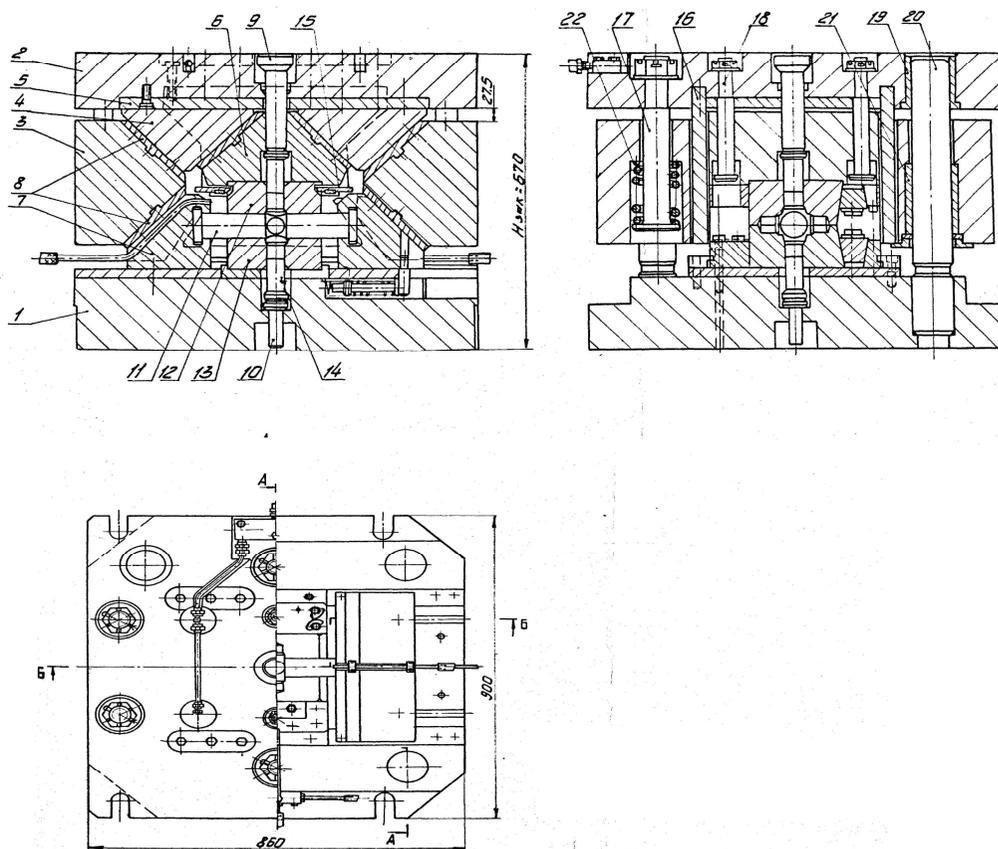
Пакет для безоблойной штамповки крестовины карданного вала
